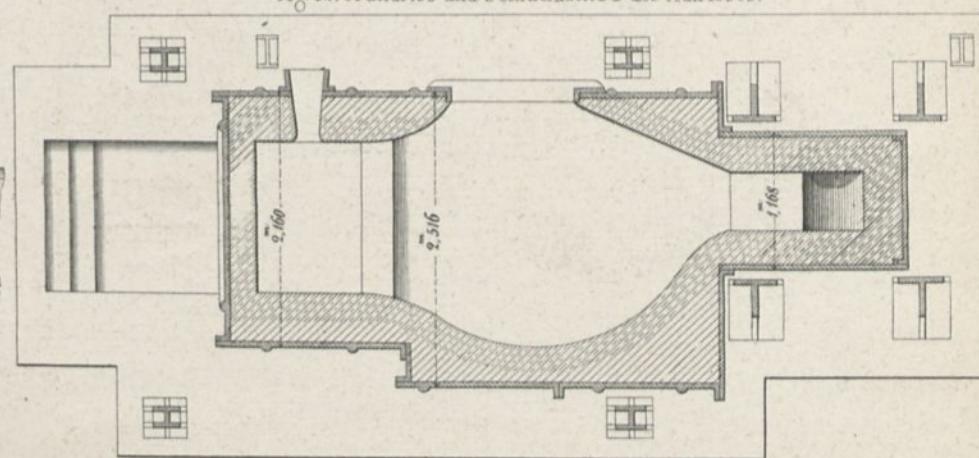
Grundriss und Schnitt nach B-B des Aufrisses.
